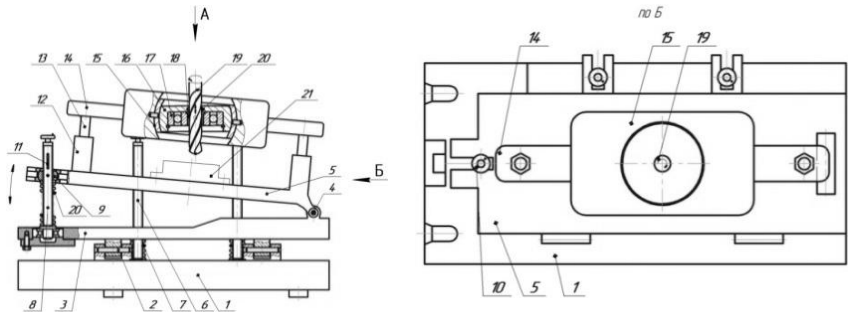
Конструкція поворотного свердлильного кондуктора
